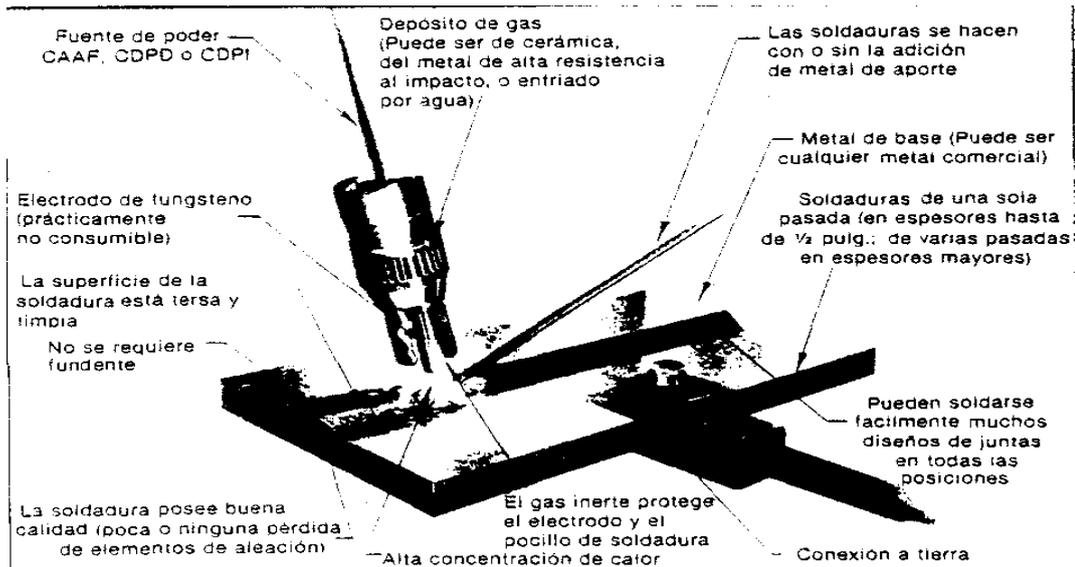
Elementos y aspectos esenciales del proceso de soldadura TIG (Tomada del manual de Soldadura Tomo I de Horwitz).
